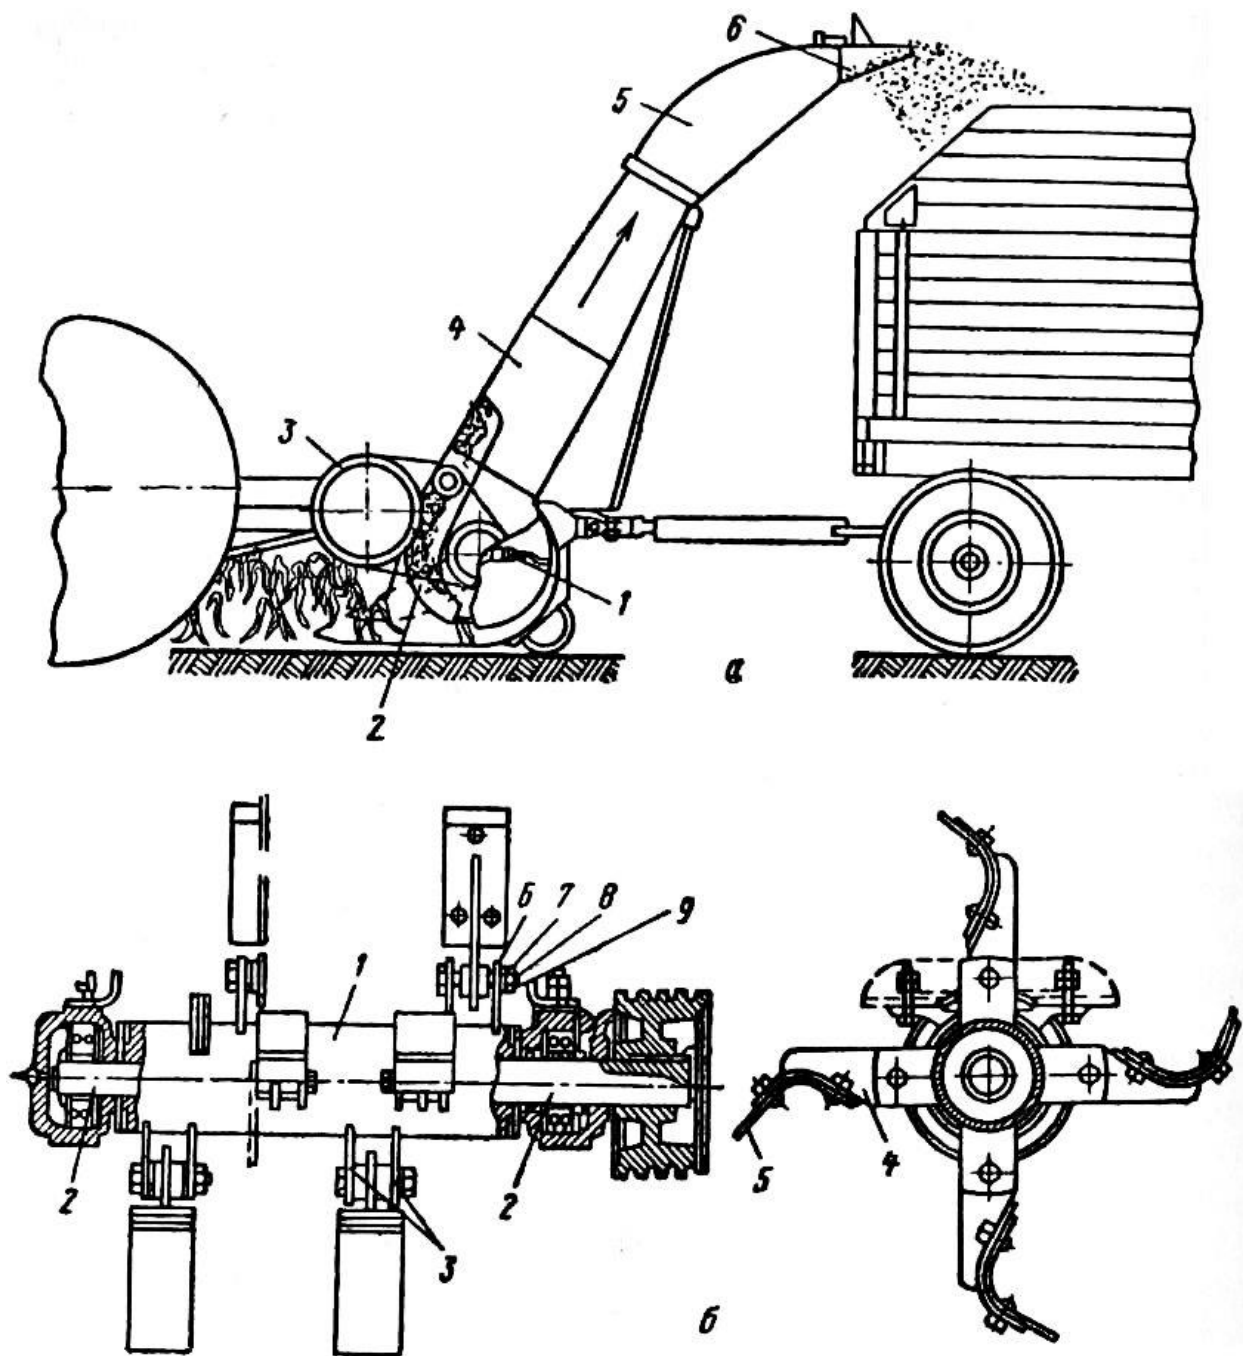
Косилка-измельчитель КИР-1,5: а – схема косилки; 1 – измельчающий барабан; 2 – передний щит; 3 – передаточный механизм; 4 – направляющая труба; 5 – поворотная секция; б – козырек; б – измельчающий барабан; 1 – труба; 2 – цапфа; 3 – проушины; 4 – кронштейн; 5 – нож; 6 – втулка; 7 – болт; 8 – гайка; 9 – шайба пружинная
